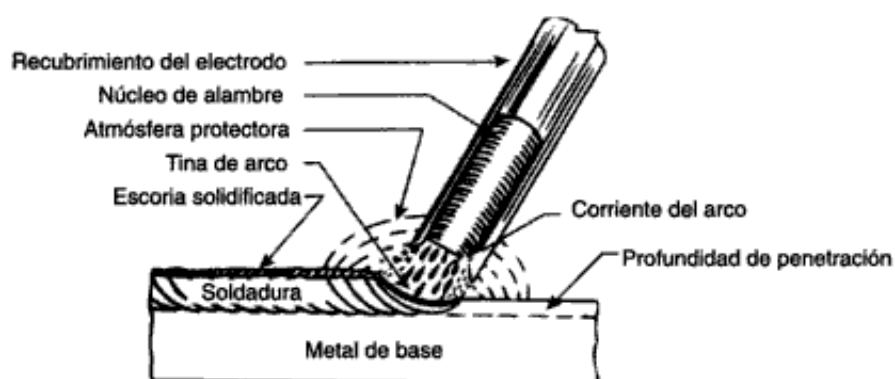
Esquema de *Shield Metal Arc Welding* (SMAW)
